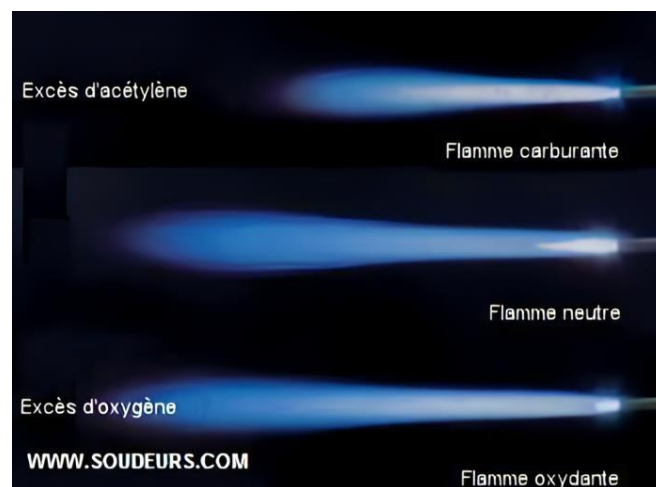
Les trois types de flamme pour le soudage oxyacétylénique.
